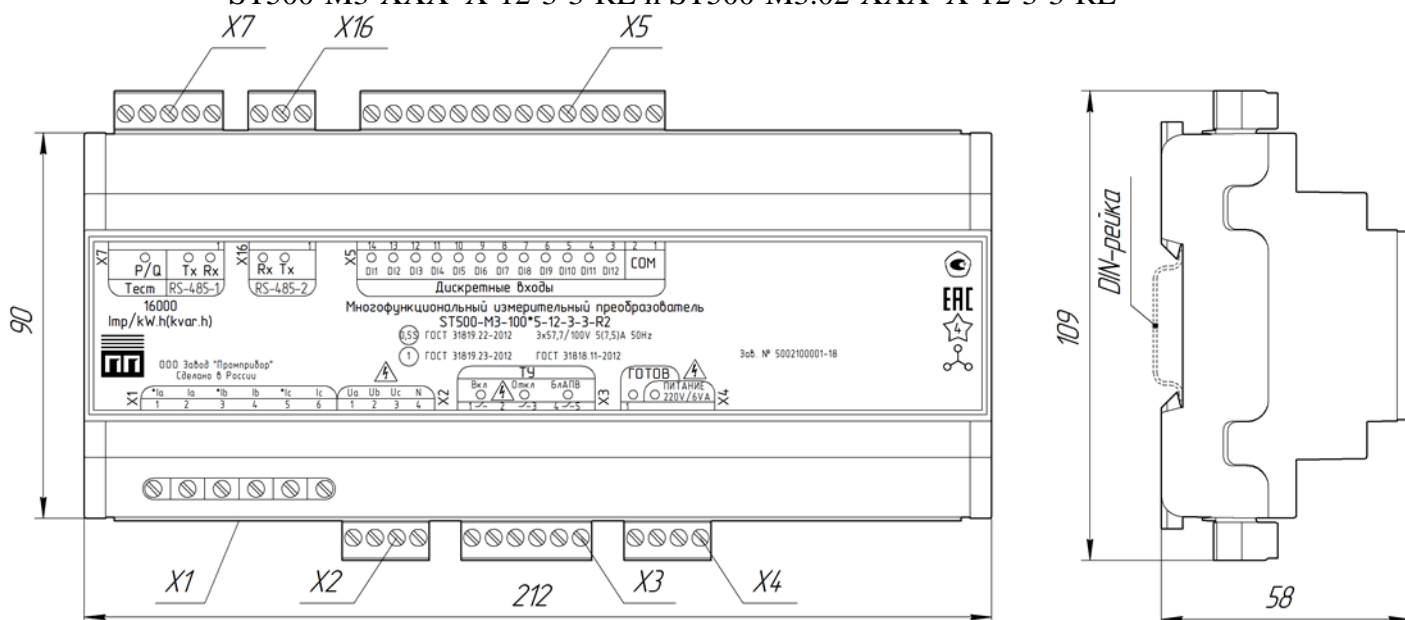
Внешний вид и габаритные размеры МИП ST500-M3-XXX*X-12-3-3-R2 и ST500-M3.02-XXX*X-12-3-3-R2
